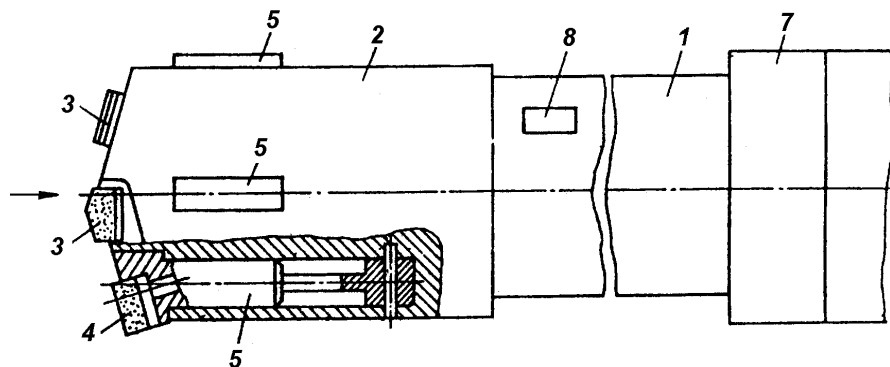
Пристрій для свердління глибоких отворів
